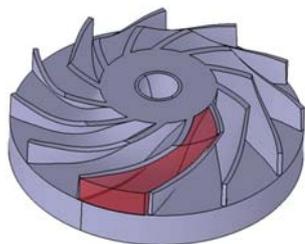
Veine fluide ouverte d'un turbocompresseur
